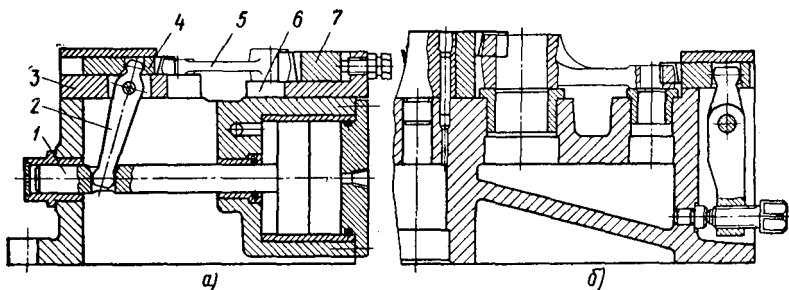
Приспособления к наладке для многопозиционной обработки: *а* — с пневматическим креплением заготовок; *б* — с винтовым креплением заготовок
